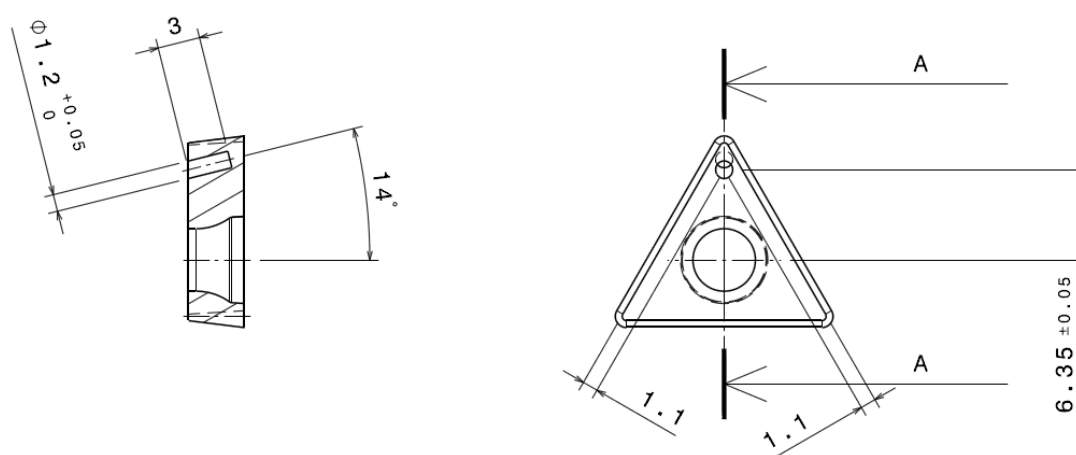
Positions des trous sur la plaquette de coupe WIDIA TCMT16T308 pour l'installation des thermocouples (dimensions en mm)
